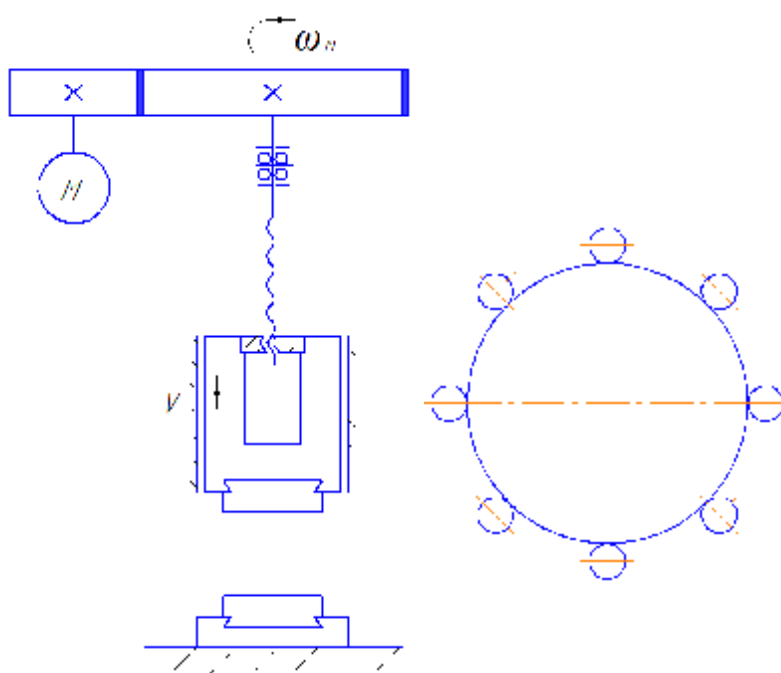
Схема винтового пресса с зубчатым приводом
